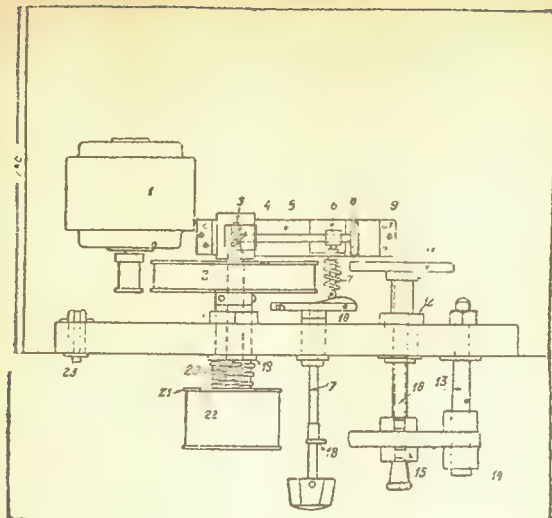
Общее расположение деталей: 1—мотор; 2 — шкив-маховик; 3 и 4 — червяк и шестерня механизма смещения рекордера; 5 — вал резинового ролика; 6 — подшипник вала резинового ролика; 7—пружина, прижимающая ролик к диску; 8 — резиновый ролик; 9 — планка крепления резинового ролика; 10 — приспособление в переключателе, отжимающее резиновый ролик; 11 — фрикционный диск; 12 — подшипник винта смещения; 13 — направляющий палец; 14 — направляющая втулка; 15 — гайка смещения рекордера; 16 — винт смещения рекордера; 17 — валек переключателя; 18 — эксцентрик, поднимающий рекордер; 19 — флянец на валу барабана, предохраняющий его от аксиальных качаний; 20 — пружина, прижимающая подвижную щеку барабана; 21 — пружинная щека; 22 — барабан
